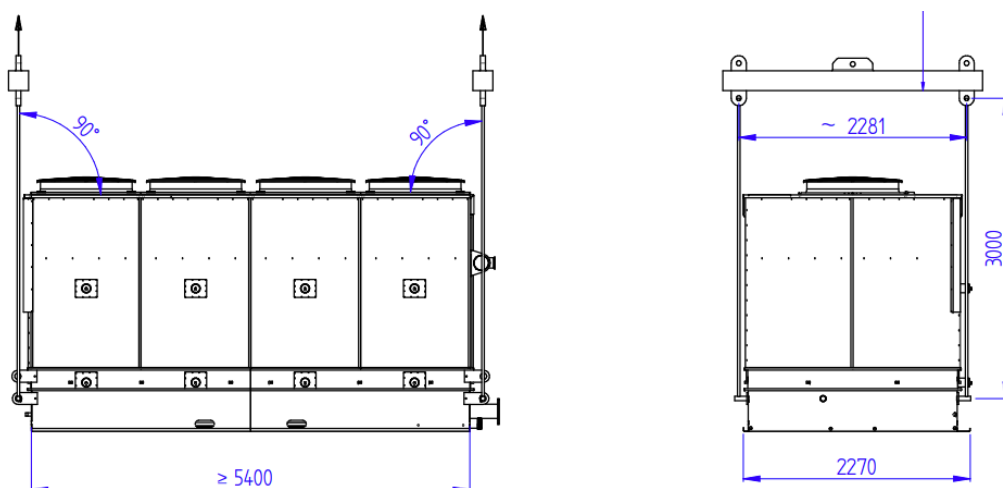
Instruções de movimentação para equipamentos com mais de 4400 mm de comprimento.
